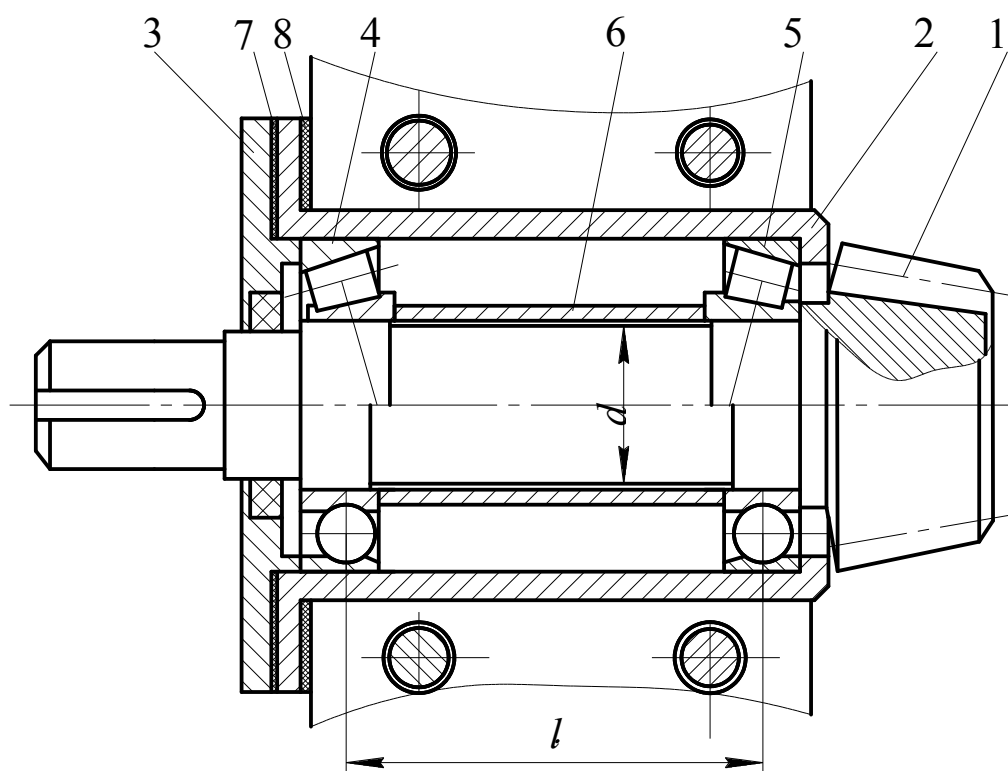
Конструкция подшипникового узла конической шестерни
